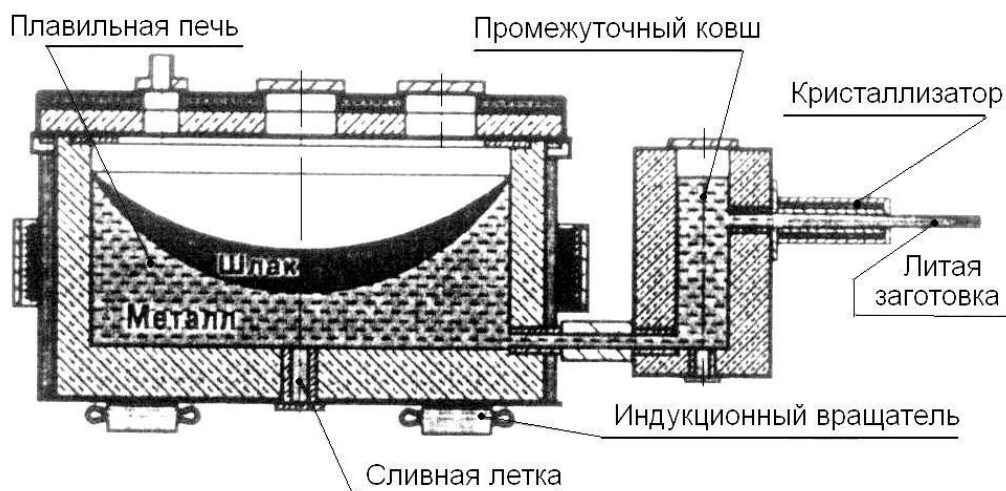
Индукционный плавильный агрегат, совмещенный с промежуточным ковшом
